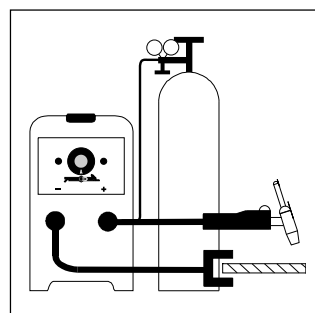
TP 1400 MV ausgerüstet zum WIG-Schweißen
